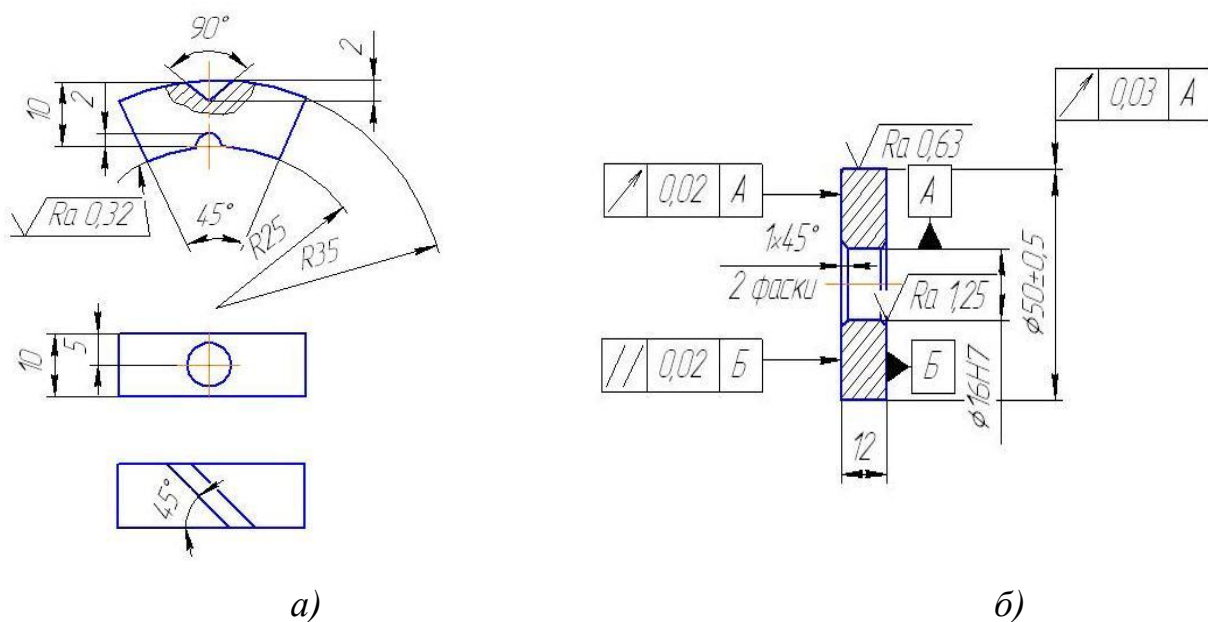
Геометрические размеры колодки (а) и ролика (б)
